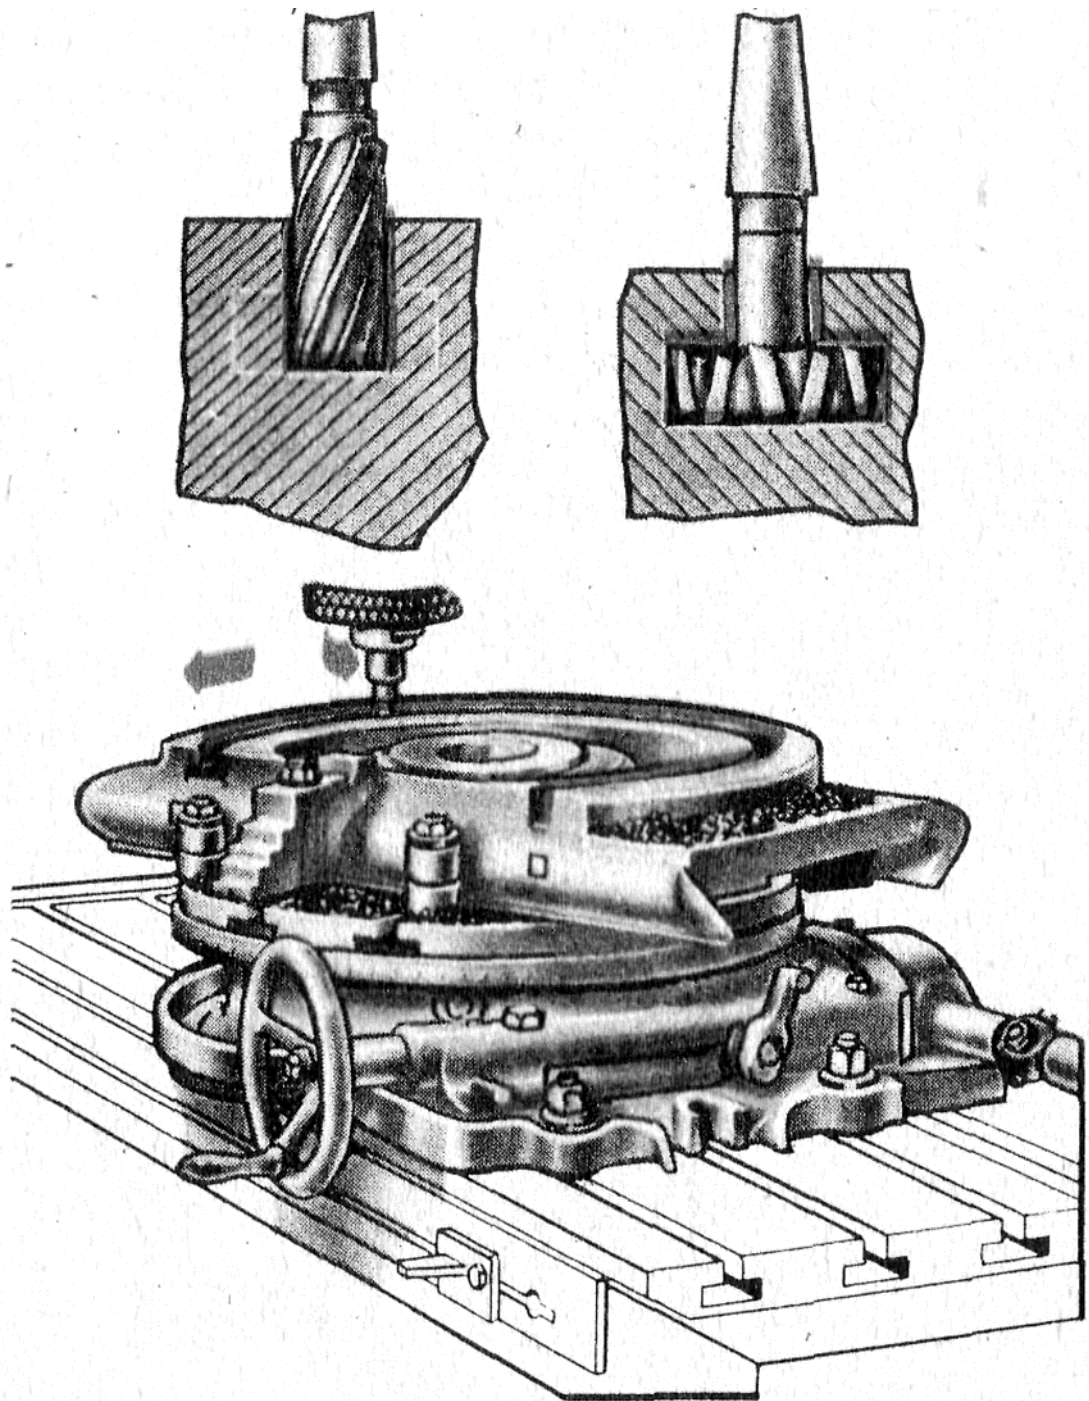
Фрезерування Т-подібного пазу.
